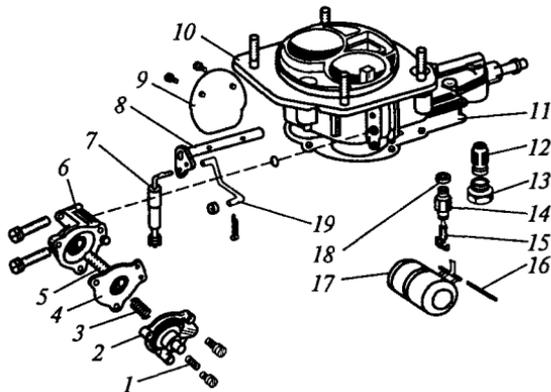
Детали крышки карбюратора 1205-1107010:
